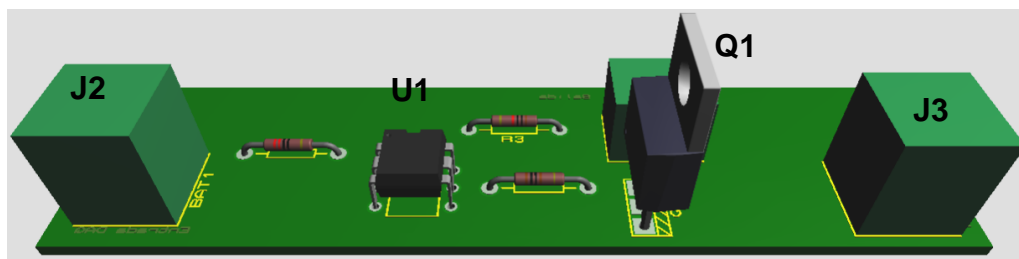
Diseño del PCB en 3D del circuito para el control de temperatura de las cámaras.
